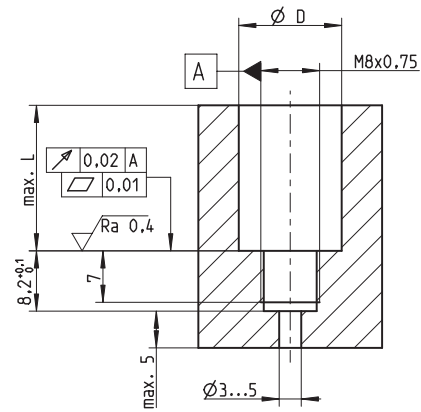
Einbau zurückversetzt. Bohrung  $\varnothing$  gemäß Werkzeug Bild 5 oder Bild 6
